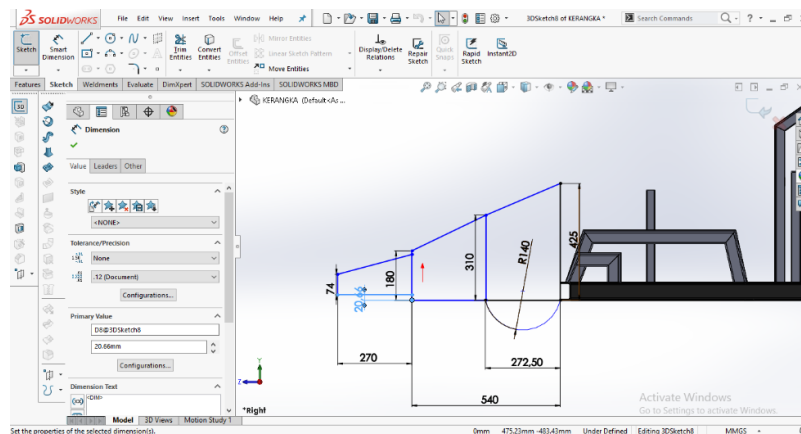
Extruded Boss/Base* Pelat Penutup Conveyor
